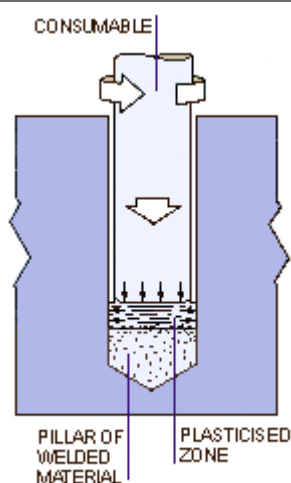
Ilustração do processo de soldagem FHP (TWI, 2016).
